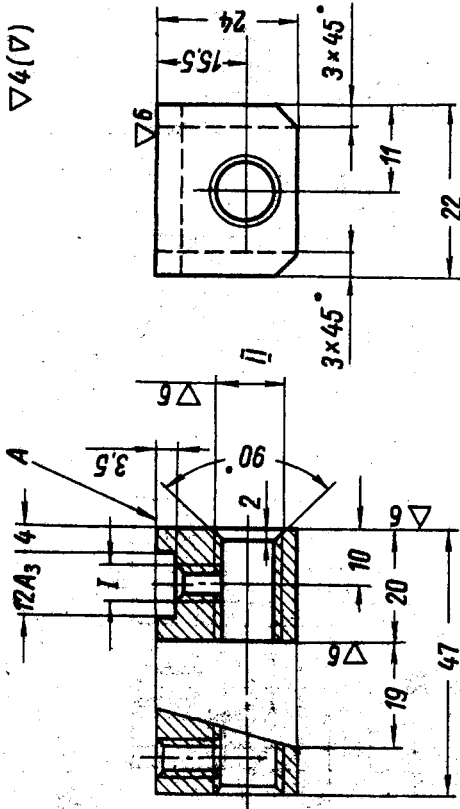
Гайка, деталь № УОЗЦ.35.40;
